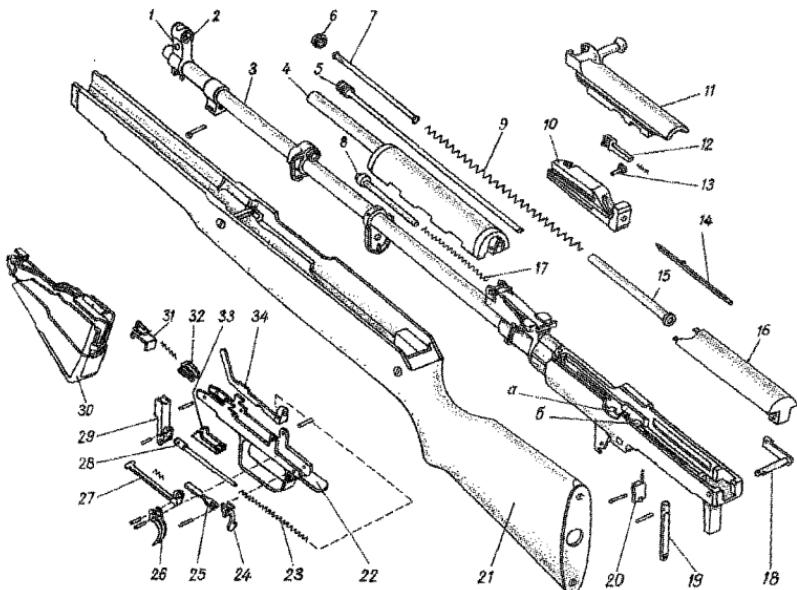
Детали карабина СКС: 1 – полозок мушки; 2 – мушки; 3 – ствол со ствольной коробкой; 4 – газовая трубка; 5 – шток с поршнем; 6 – замыкатель возвратной пружины; 7 – направляющий стержень; 8 – толкател; 9 – возвратная пружина; 10 – затвор; 11 – затворная рама; 12 – выбрасыватель; 13 – шпилька; 14 – ударник; 15 – направляющая трубка; 16 – крышка ствольной коробки; 17 – пружина толкателя; 18 – чека крышки ствольной коробки; 19 – защелка предохранительной скобы; 20 – затворная задержка с пружиной; 21 – ложа; 22 – предохранительная скоба; 23 – боевая пружина; 24 – предохранитель; 25 – пружина предохранителя; 26 – спусковой крючок; 27 – спусковой рычаг; 28 – направляющий стержень; 29 – курок; 30 – магазин; 31 – защелка крышки магазина; 32 – шептало; 33 – разобщитель; 34 – автоспуск; «а» – отражатель; «б» – боевой упор.
